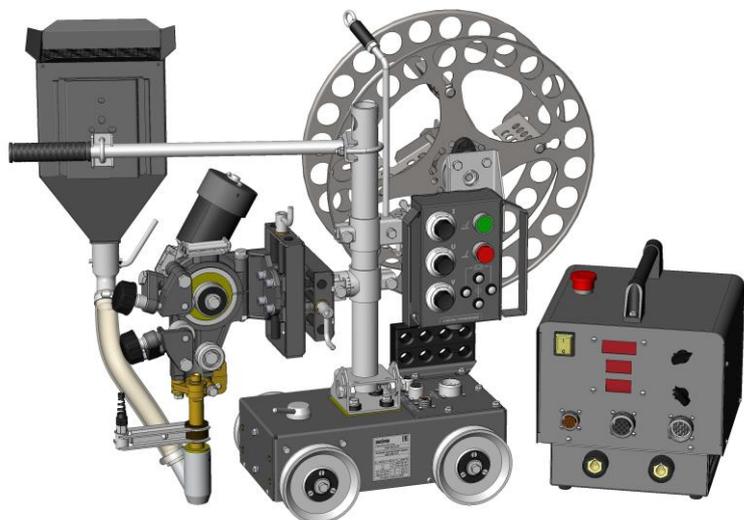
Автомат сварочный АДФ-1000-А исп.00
